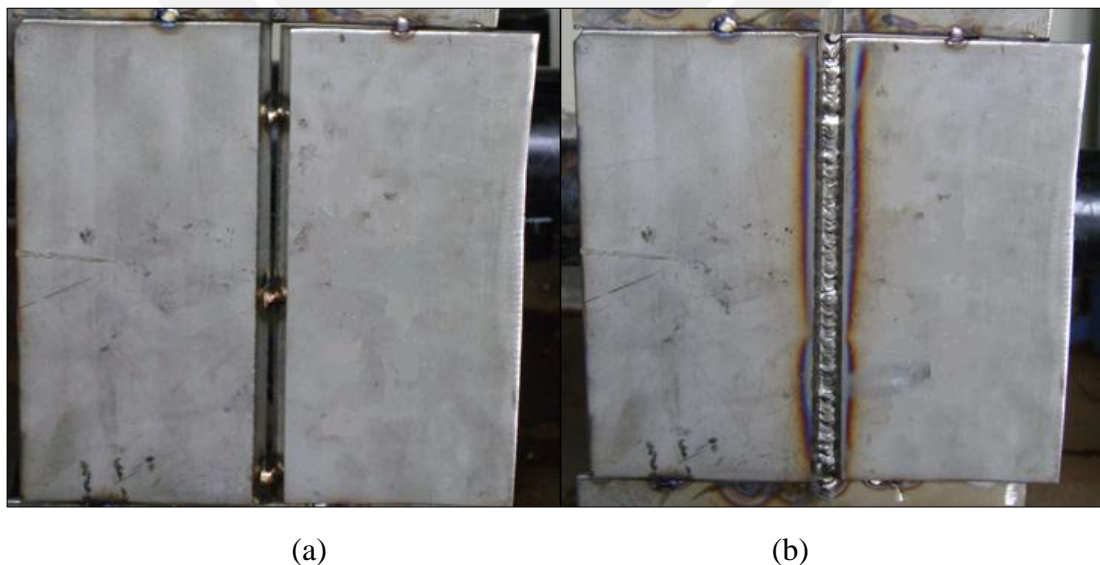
(a) Cupón de soldadura apuntalado. (b) inspección visual de la raíz.
